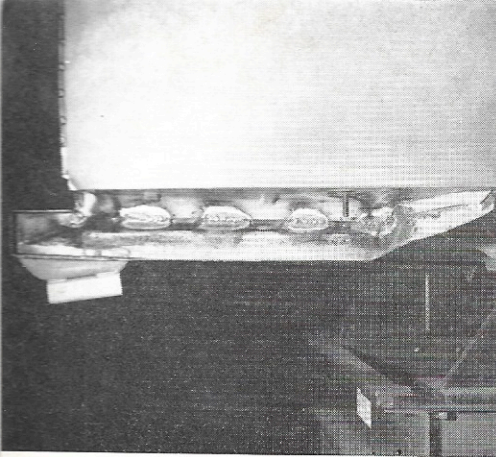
Soudage à la soudure oxyacétylénique de l'aile arrière avec le passage de roue.
